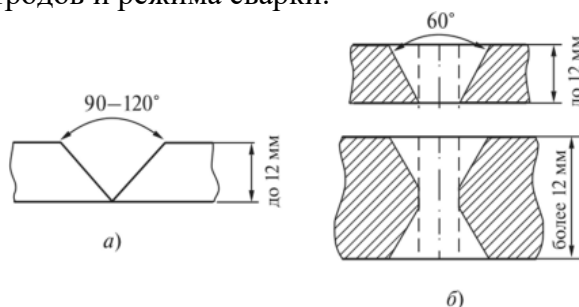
Подготовка трещины (а) и отверстия (б) к заварке
